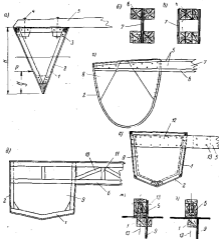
Конструкции поперечных мостиков: а — балочный разъемный мостик (конец корпуса); б — фанерная балка двутавровой конструкции; в — фанерная балка коробчатой конструкции; г — балочный неразъемный мостик; д — рамный мостик; е — балочный разъемный мостик; ж, з — крепление балки к веревке в бочку
